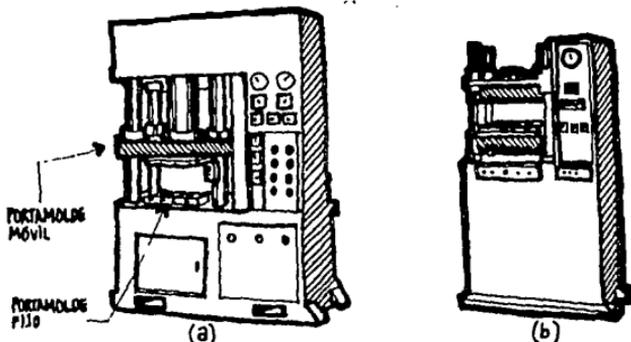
Máquina de Compresión a).- De producción b).- De laboratorio
